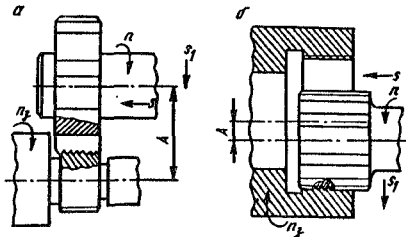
Схемы фрезерования резьбы групповой (гребенчатой) фрезой на цилиндрических поверхностях: а — наружных; б — внутренних
